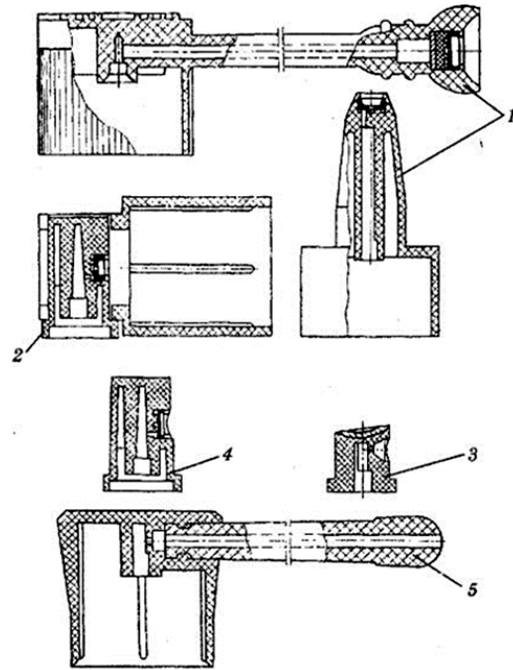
Види розпилювачів і насадок на аерозольних балонах
